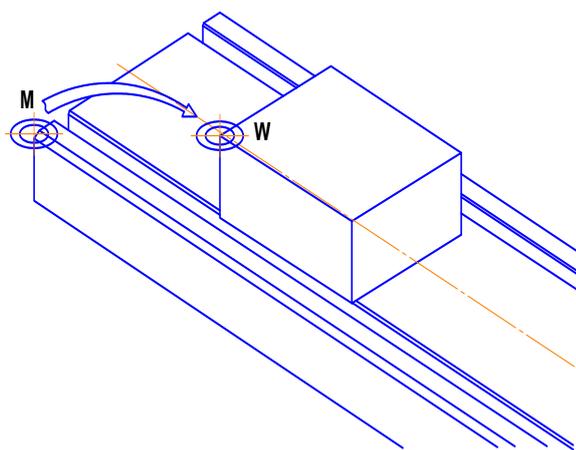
Сдвиг станочного нуля M в нуль детали W
